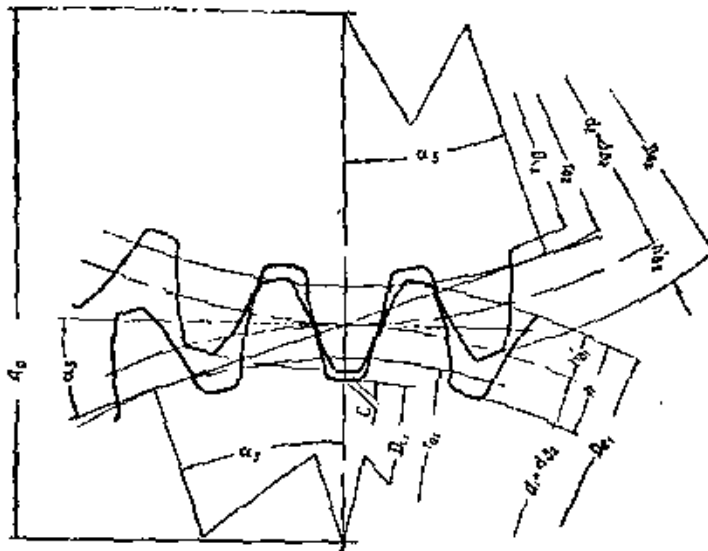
Цилиндрические зубчатые колеса наружного зацепления.
